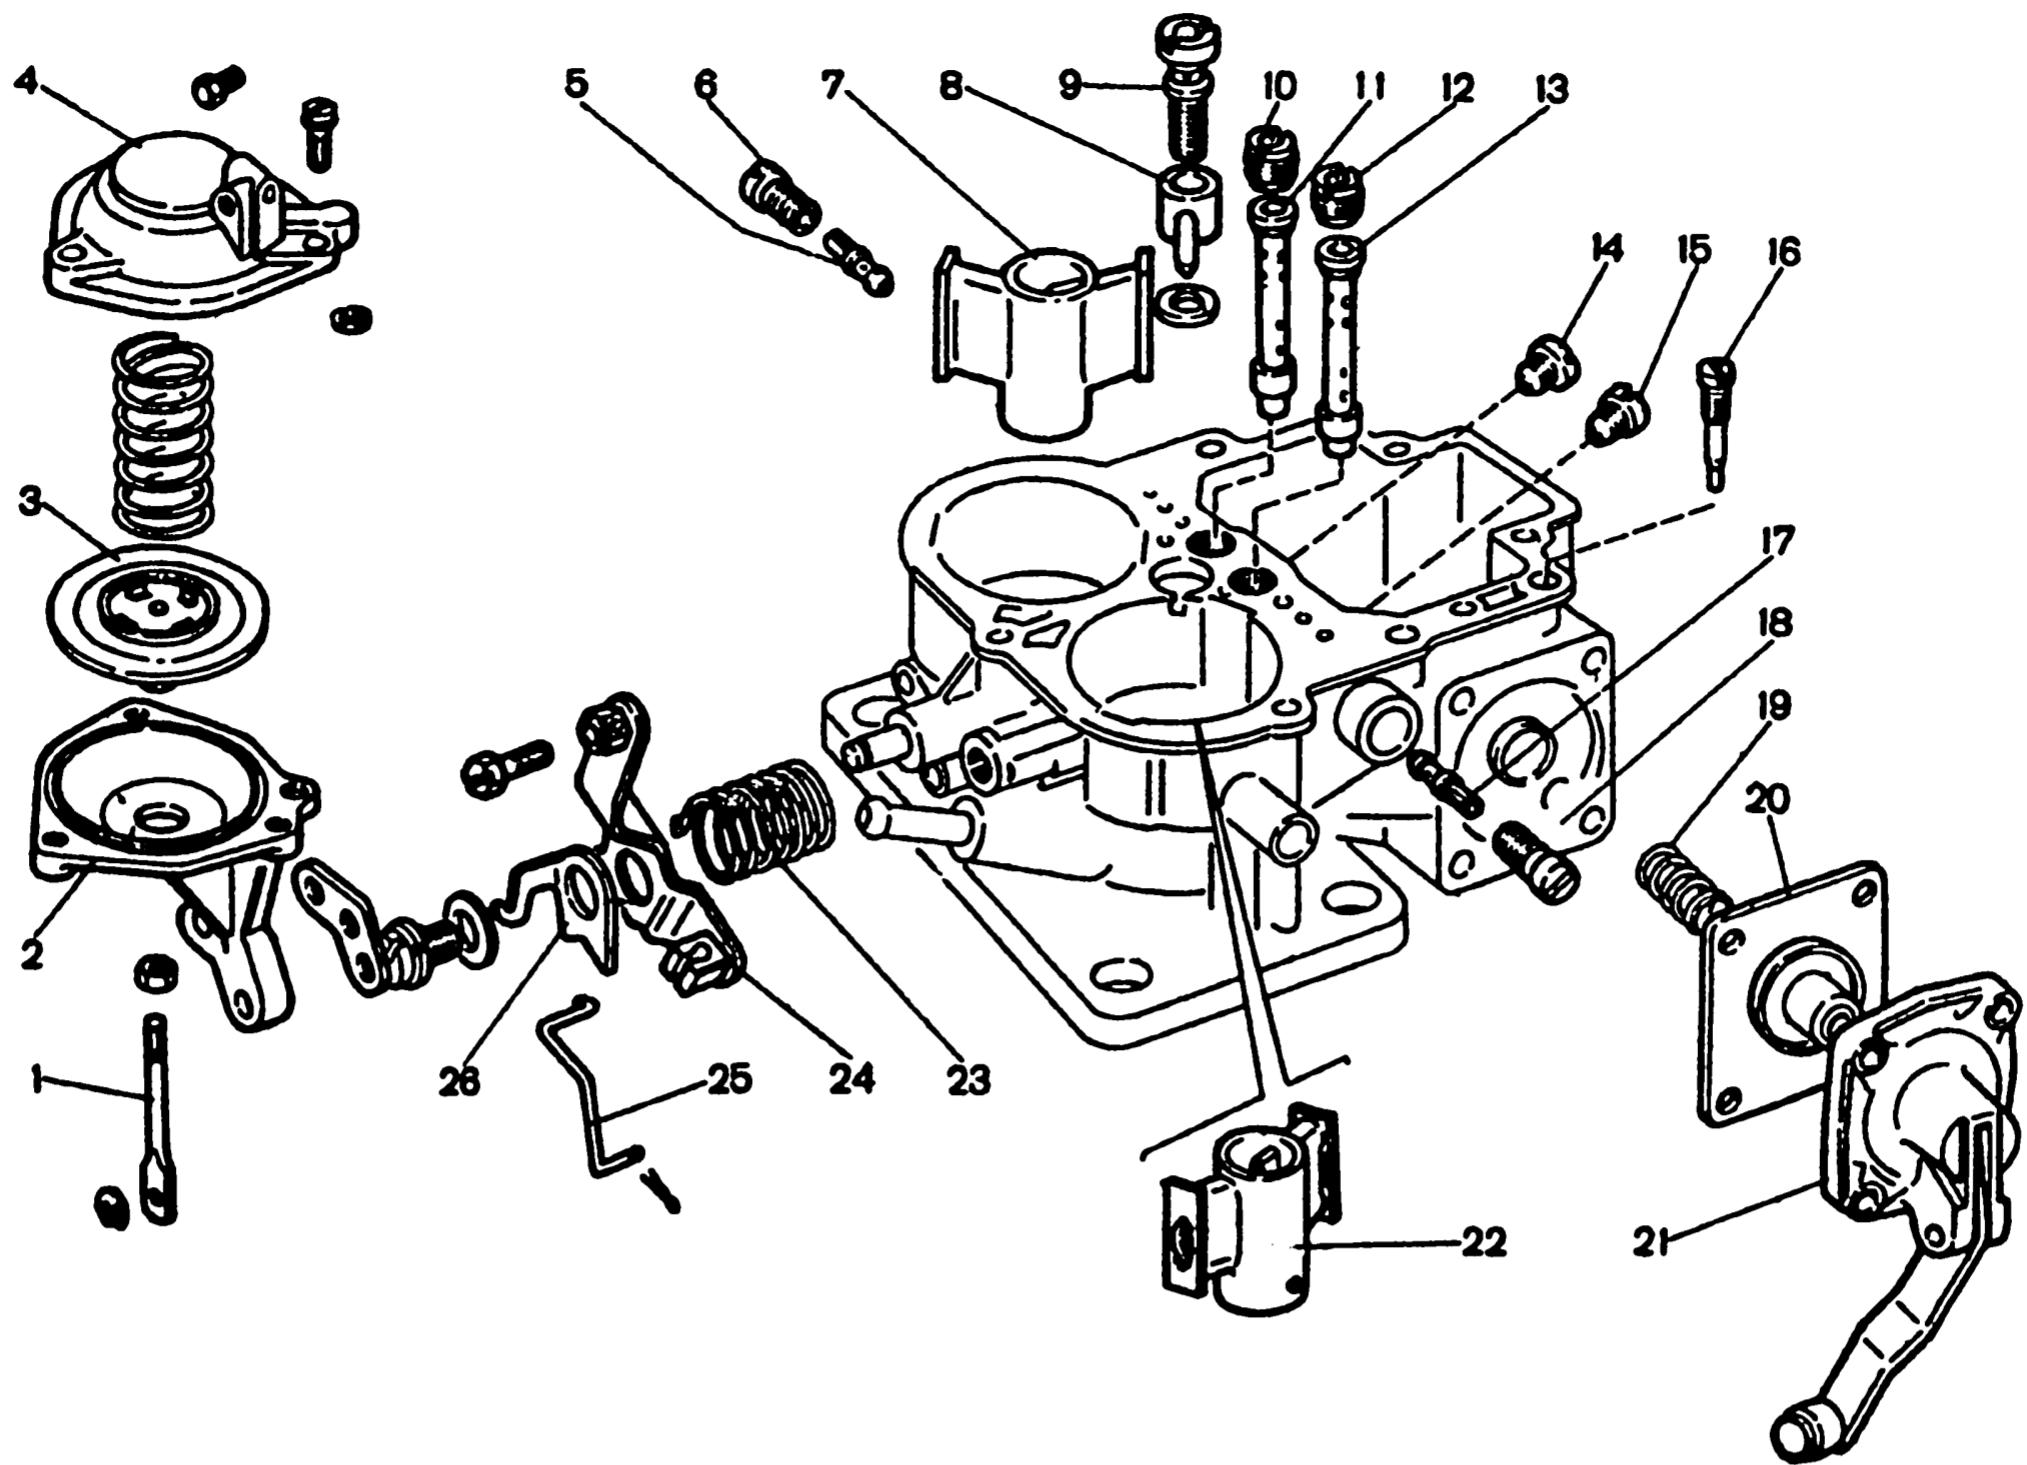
Детали корпуса карбюратора 2105-1107010: 1 - шток пневмопривода второй дроссельной заслонки; 2 - корпус пневмопривода; 3 - диафрагма; 4 - крышка пневмопривода; 5 - топливный жиклер переходной системы второй камеры; 6 - корпус топливного жиклера; 7 - малый диффузор второй камеры; 8 - распылитель ускорительного насоса; 9 - винт-клапан ускорительного насоса; 10 - главный воздушный жиклер второй камеры; 11 - эмульсионная трубка второй камеры; 12 - главный воздушный жиклер первой камеры; 13 - эмульсионная трубка первой камеры; 14 - главный топливный жиклер второй камеры; 15 - главный топливный жиклер первой камеры; 16 - регулировочный винт ускорительного насоса; 17 - топливный жиклер системы холостого хода; 18 - корпус топливного жиклера; 19 - возвратная пружина ускорительного насоса; 20 - диафрагма ускорительного насоса; 21 - крышка ускорительного насоса; 22 - малый диффузор первой камеры; 23 - возвратная пружина рычага; 24 - трёхплечий рычаг привода воздушной заслонки; 25 - тяга связи с дроссельной заслонкой; 26 - кронштейн возвратной пружины дроссельных заслонок
